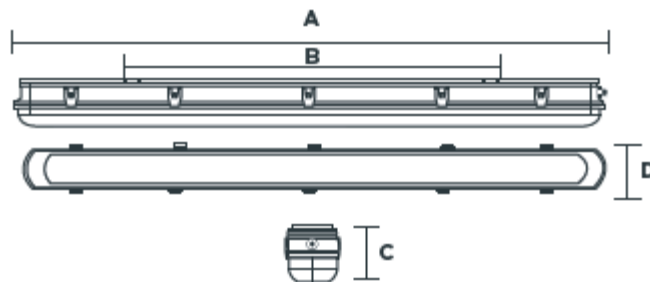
Detalles de luminaria a prueba de polvo y goteo
